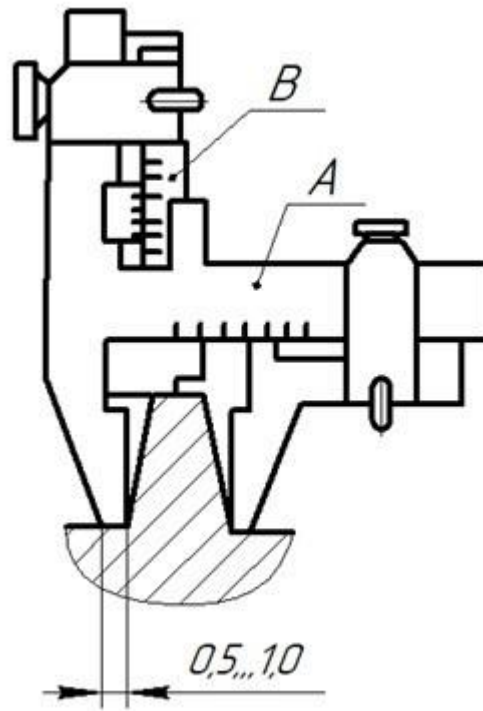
Схема вимірювання висоти зуба черв'ячної зуборізної фрези за допомогою зубоміра
